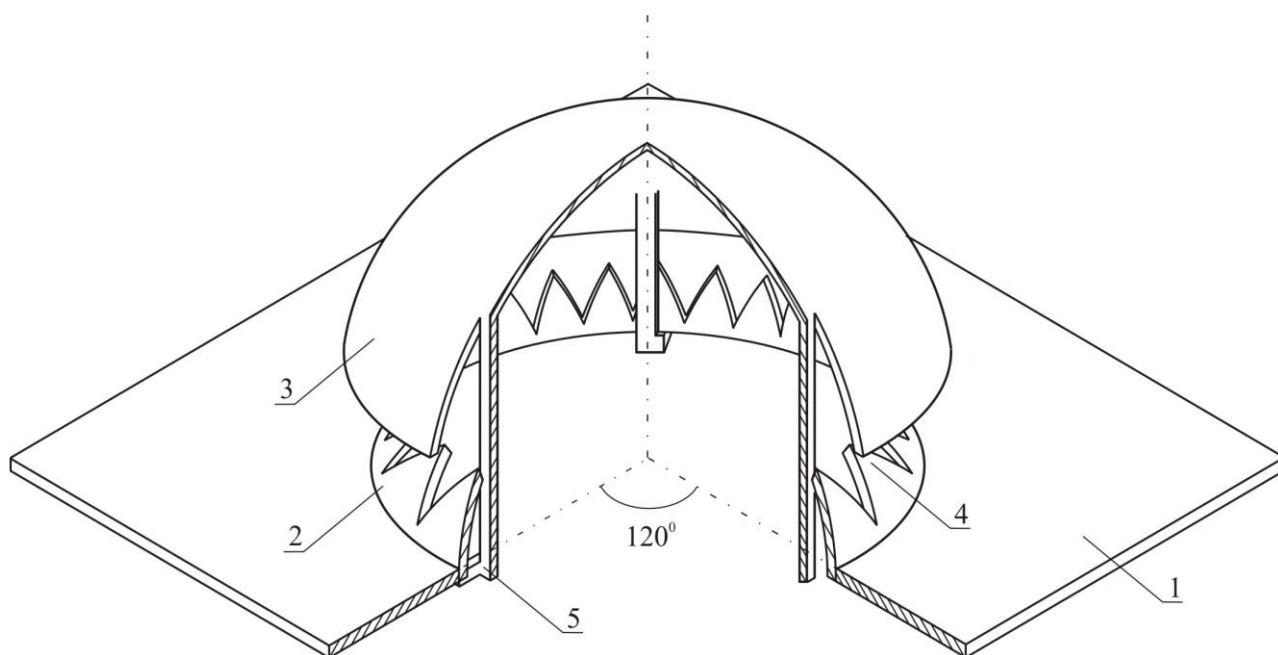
Клапанна тарілка зі сферичними клапанами: 1 – полотно; 2 – газовий патрубок; 3 – клапан; 4 – зубцюватий край газового патрубка; 5 – обмежувальні ніжки
